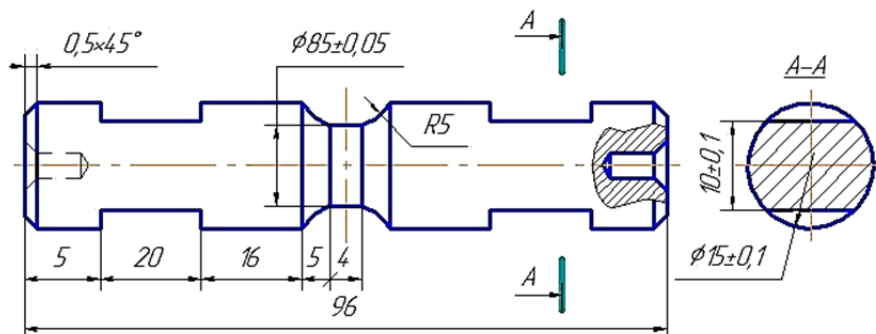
Общий вид и геометрические размеры образцов для испытаний на кручение
